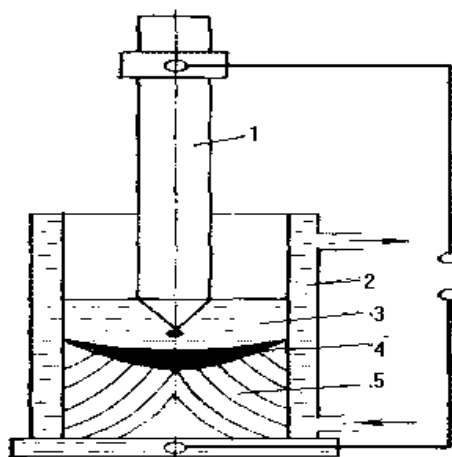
Схема установки ЕШП: 1 – електрод; 2 – кристалізатор; 3 – рідкий шлак; 4 – рідкий метал; 5 – наплавлений шар металу
